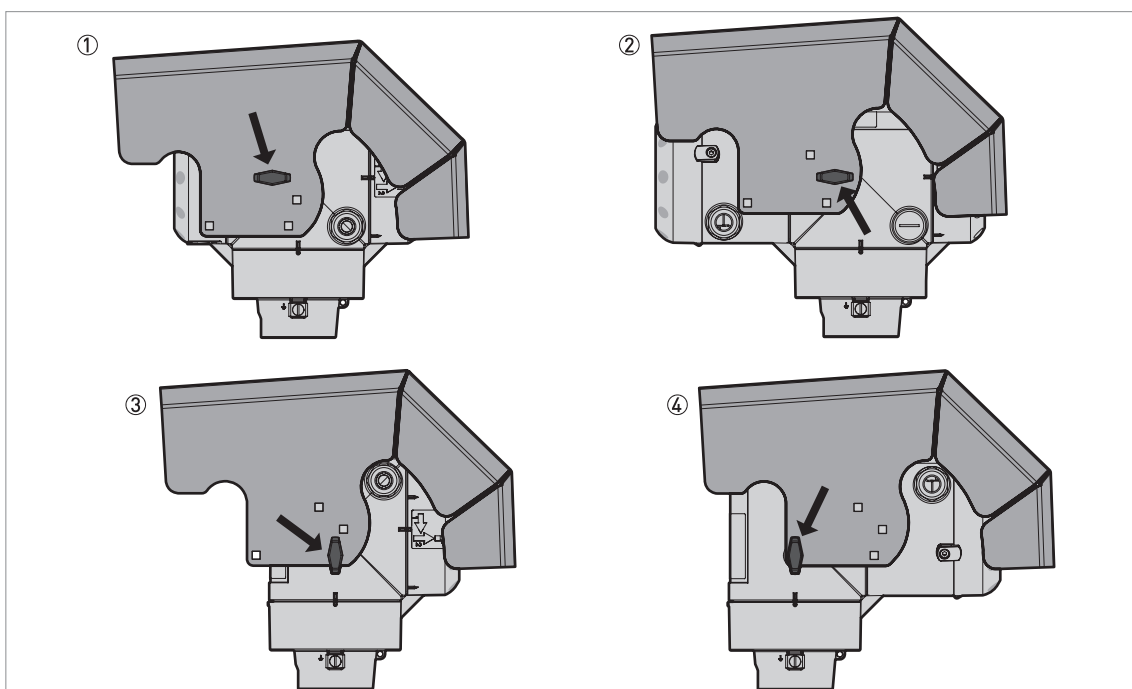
Отверстия для монтажа защитного козырька (для различных версий корпуса)
